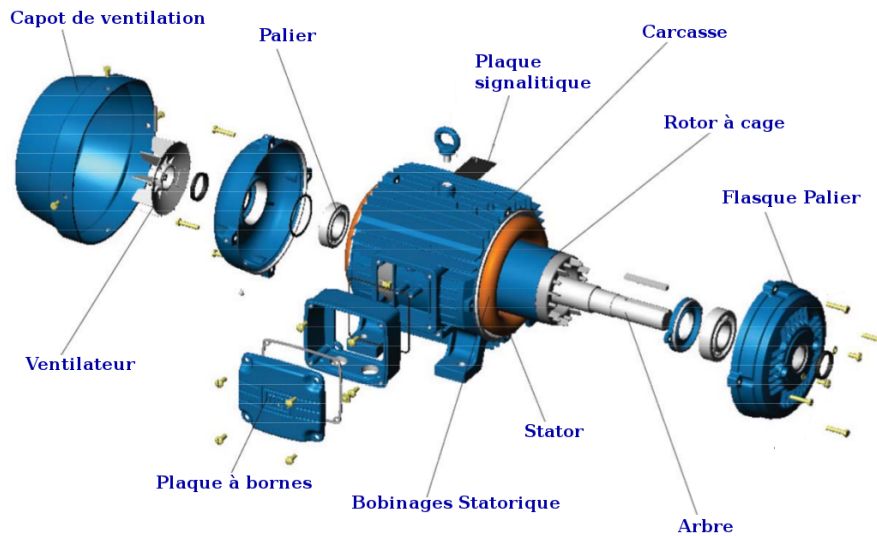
Vue éclatée du moteur asynchrone à cage
